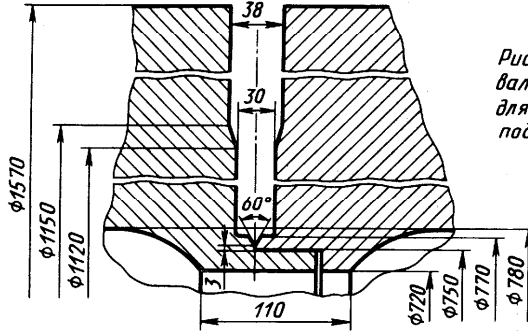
Заготовка оси опорного вала стана „5000“ в сборе для автоматической сварки под флюсом
